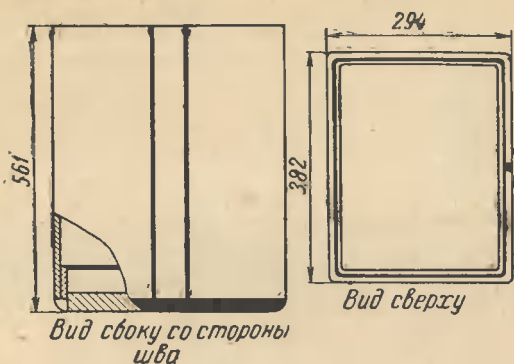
Готовый чехол-вкладыш, сделанный из жесткого винипласта.
